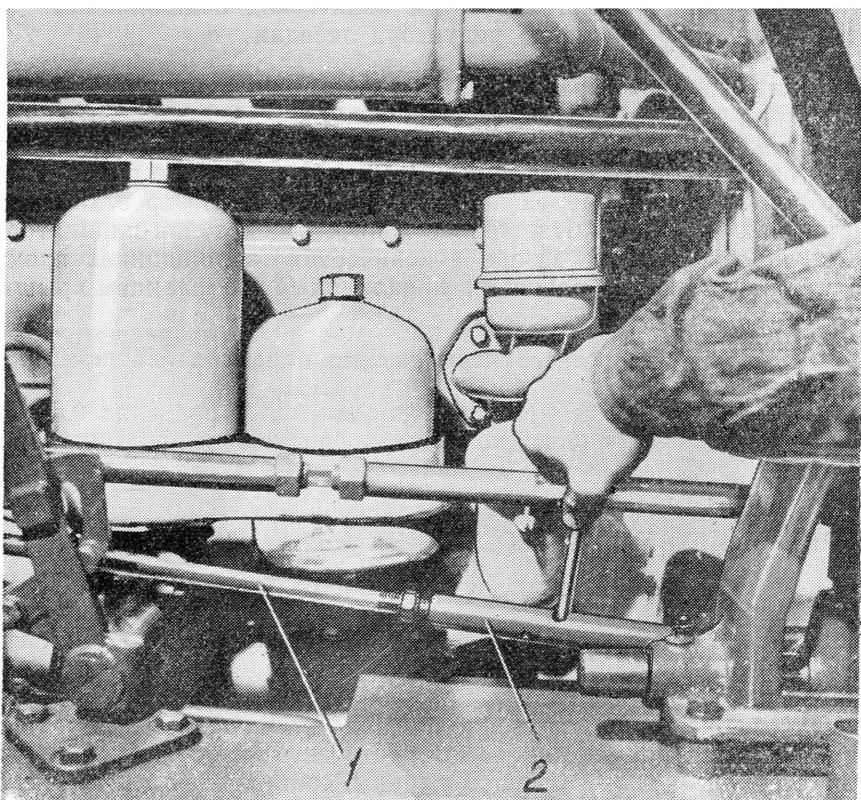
Регулировка привода управления главной муфтой сцепления:
